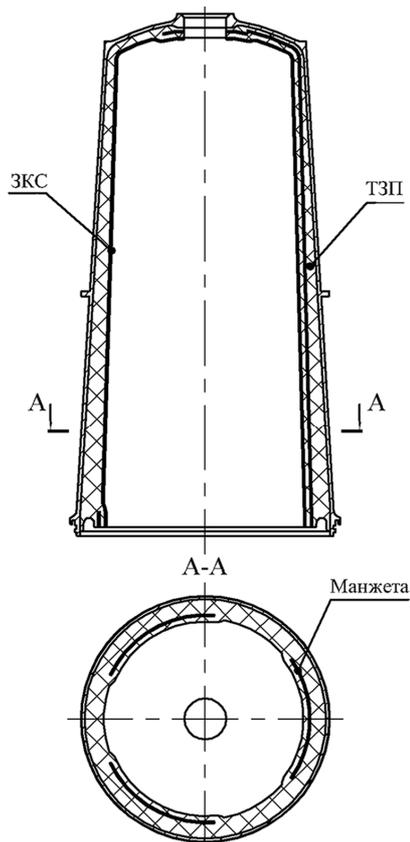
Корпус с ТЗП двигателя торцевого горения
